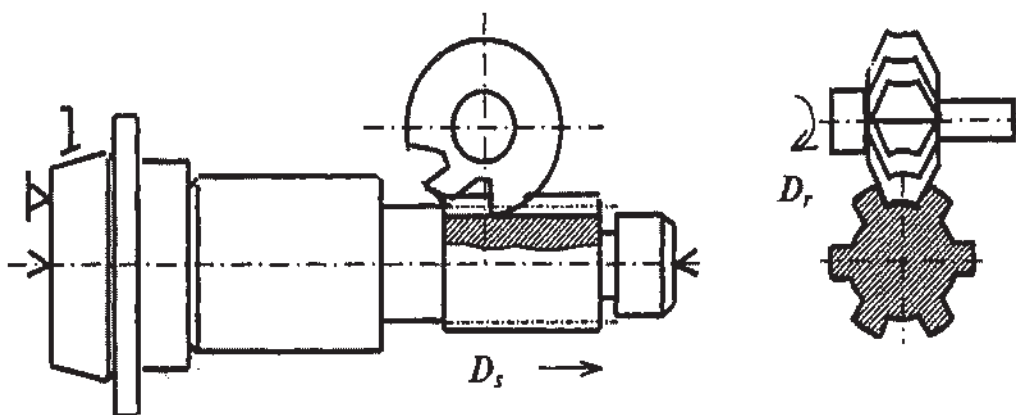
Схема обработки шлицевой поверхности дисковой фрезой
